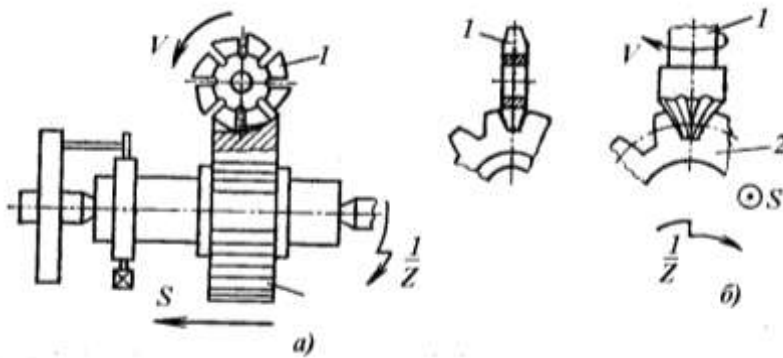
Схеми фрезерування зубців за методом копіювання
